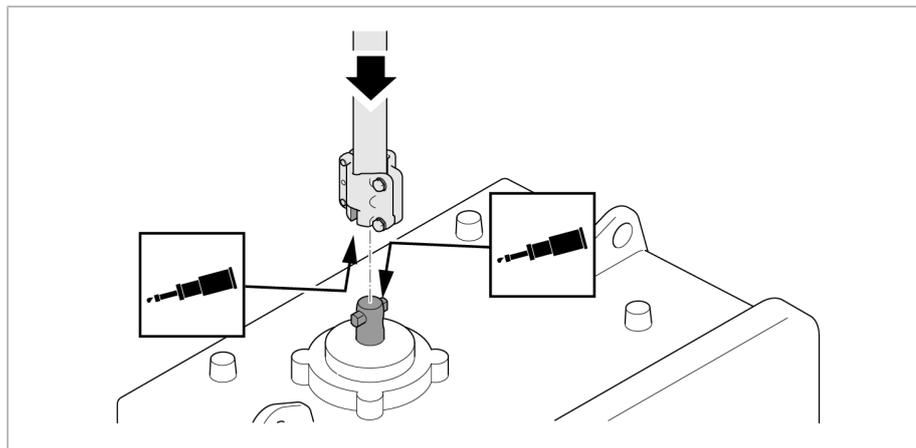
Установка четырехгранной трубы с муфтой на конец вала
